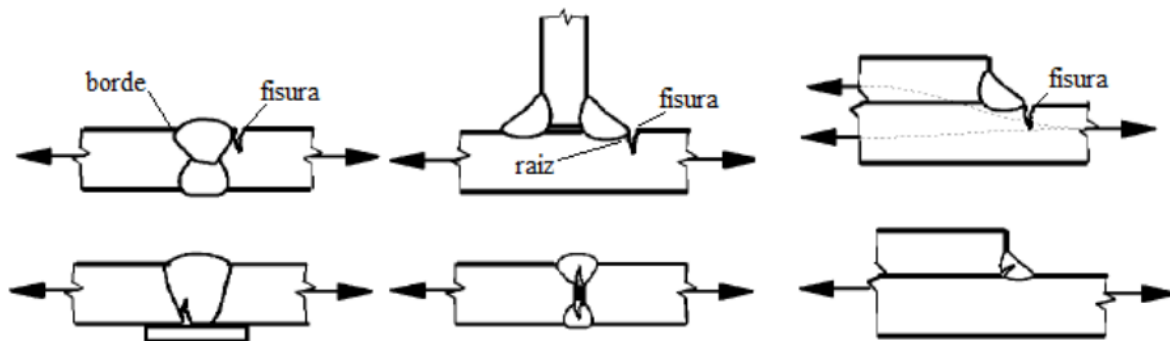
Defectos en juntas de soldaduras a tope y en T. [15]
